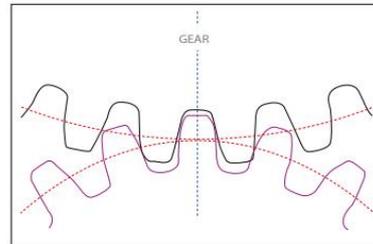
El engrane de los engranajes puede transmitir con eficacia la fuerza de rotación. El círculo rojo representa el diámetro real de la transmisión, que se llama el diámetro de paso. La forma especial de los dientes permite un engrane suave y transmite la potencia a lo largo de la transmisión.
